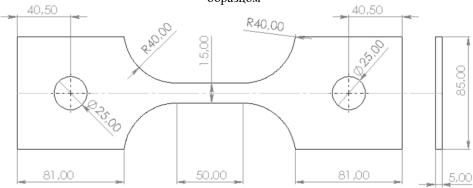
Геометрические размеры образца для испытаний на малоцикловую усталость (первая часть испытаний)
